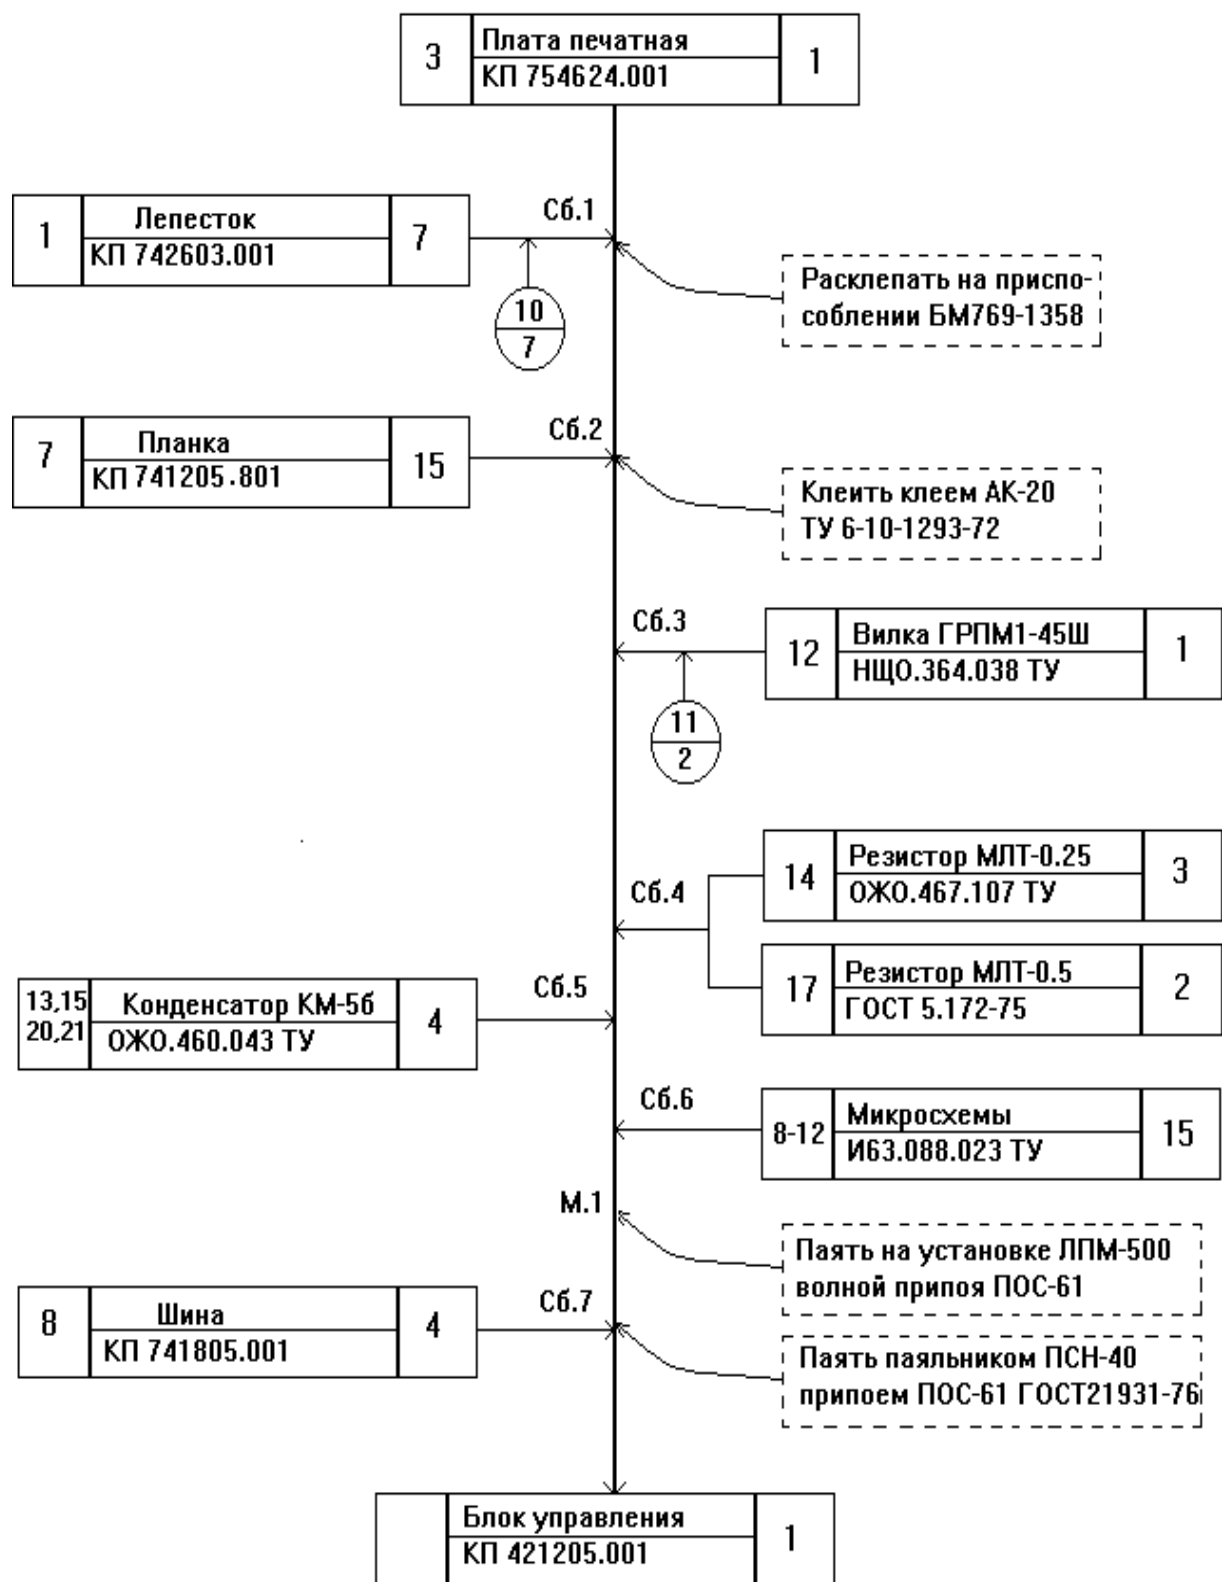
Технологическая схема сборки блока с базовой деталью
